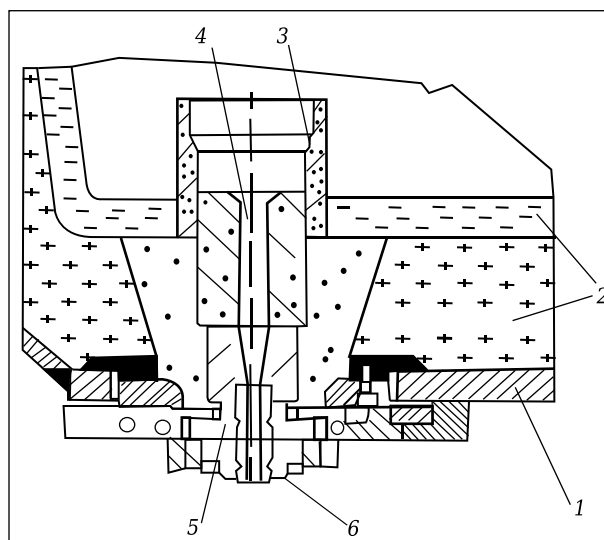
Установка оборудования разливочного отверстия со специальными стартовыми элементами стакана-дозатора
